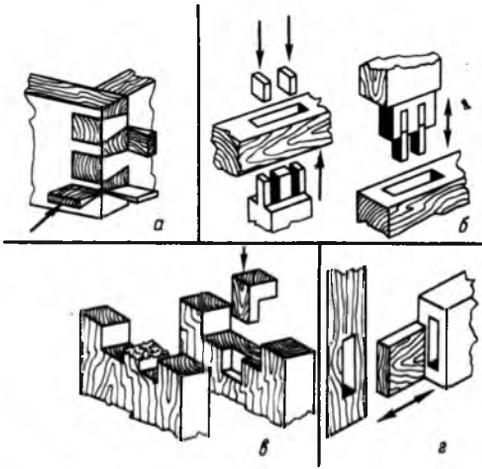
Ремонт разобранного соединения: а, б — укрепление шиповых соединений вставками; в — замена ящичного шипа; г — замена рамного шипа
